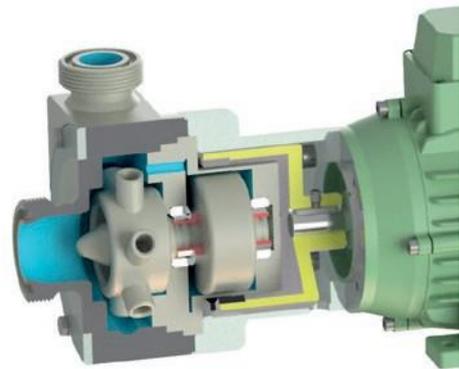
Schnittbild einer magnetgekoppelten Pumpen von Sager + Mack mit Röhrenlaufrad und Lagerbereich
